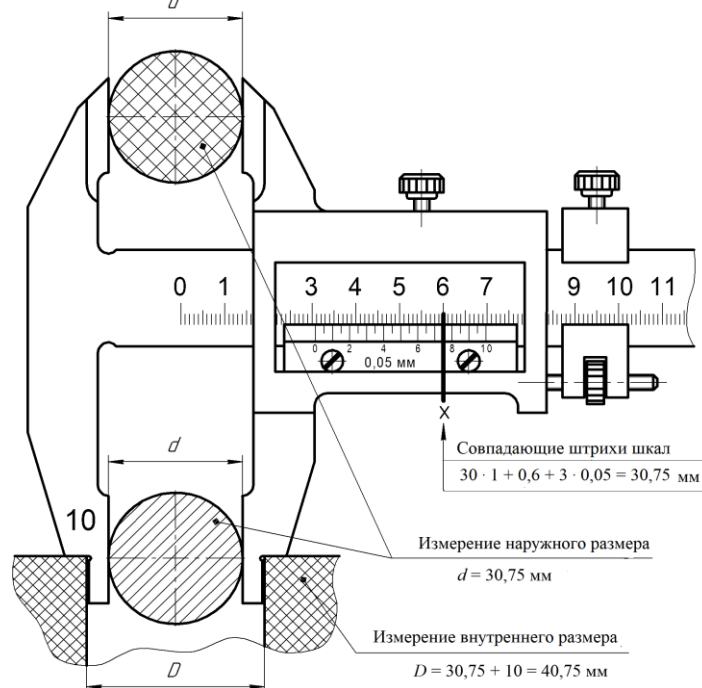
Измерение размеров деталей штангенциркулем типа II
